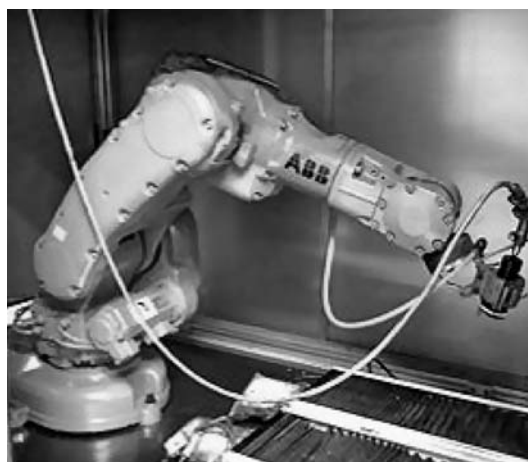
РТК лазерной сварки на базе ПР ABB IRB 140
